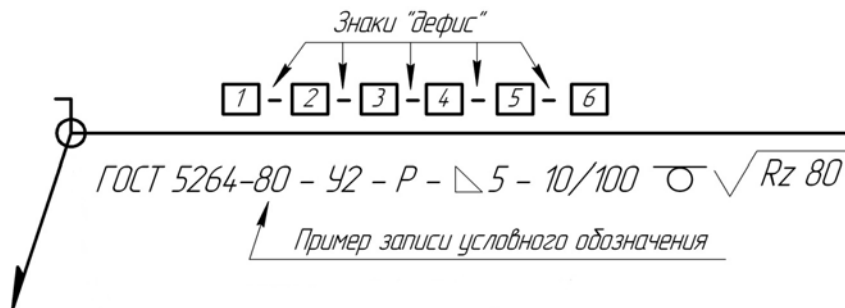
Структура условного обозначения сварного шва
